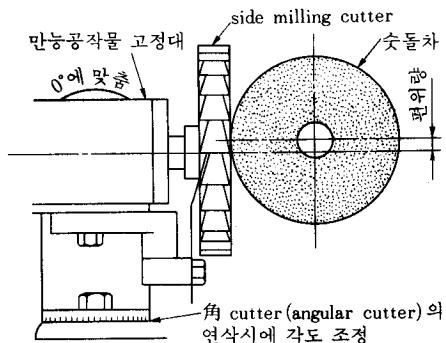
平形 칫돌에 의한 side milling cutter의側面研削
